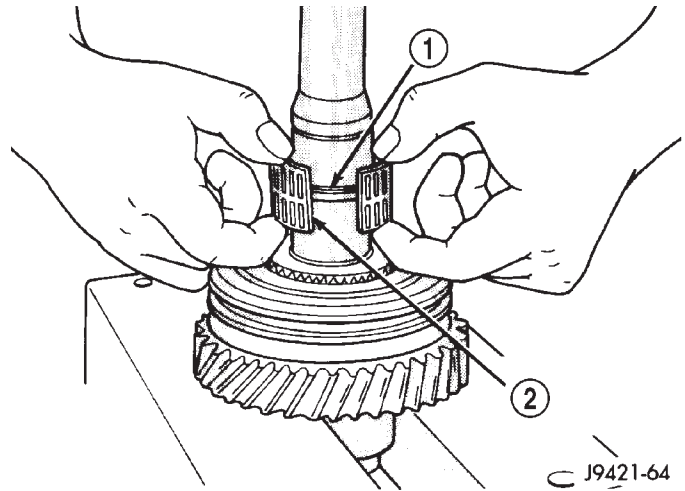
COJINETE DEL ENGRANAJE DE QUINTA
